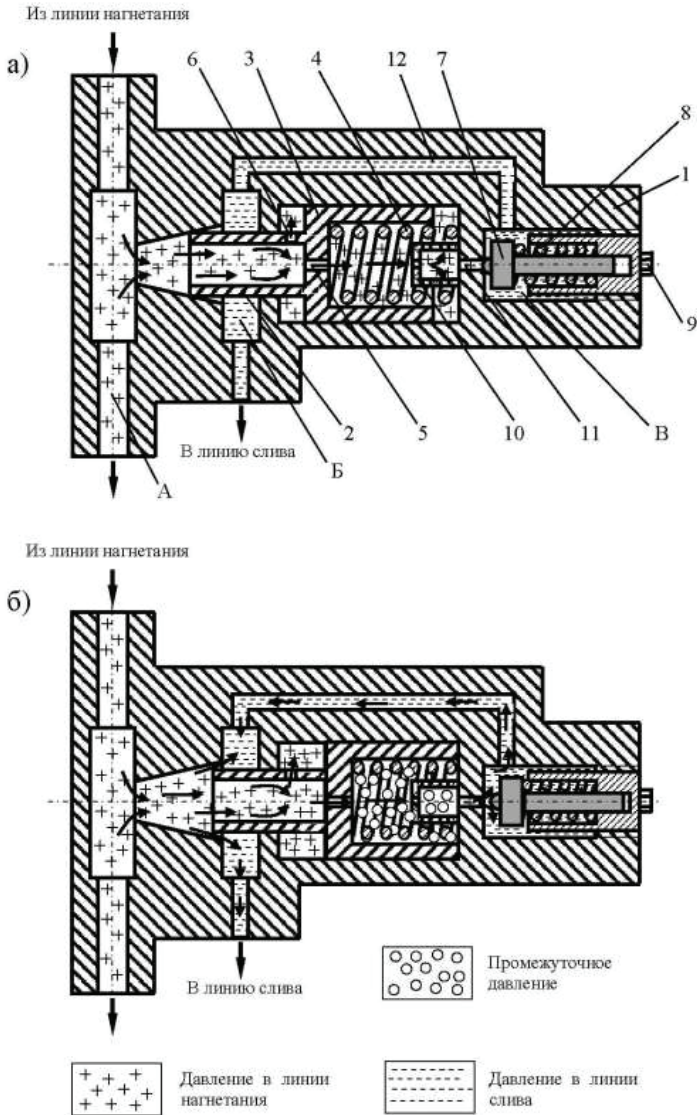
Принципиальная схема предохранительного клапана, где 1- корпус; 2- клапан; 3- поршень; 4, 8- пружина; 5, 6, 11- дроссельное отверстие; 7- шариковый клапан; 9- регулировочный винт; 10- фильтр; 12- канал; А- полость, соединенная с линией нагнетания; Б- полость, соединенная с линией слива; В- полость шарикового клапана
